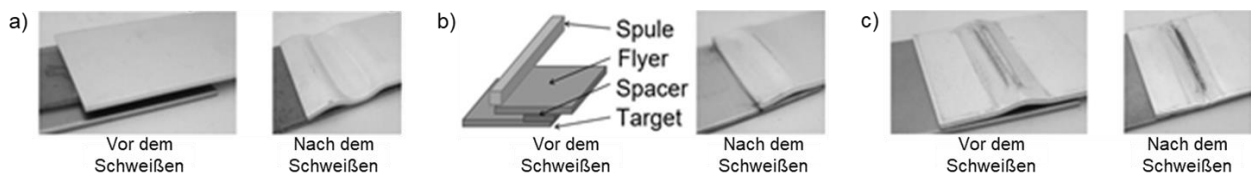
MPS mit a) Paralleler Schweißgeometrie (Standardausführung), b) einseitig einfach überhängender Schweißgeometrie und c) V-Nut Schweißgeometrie
